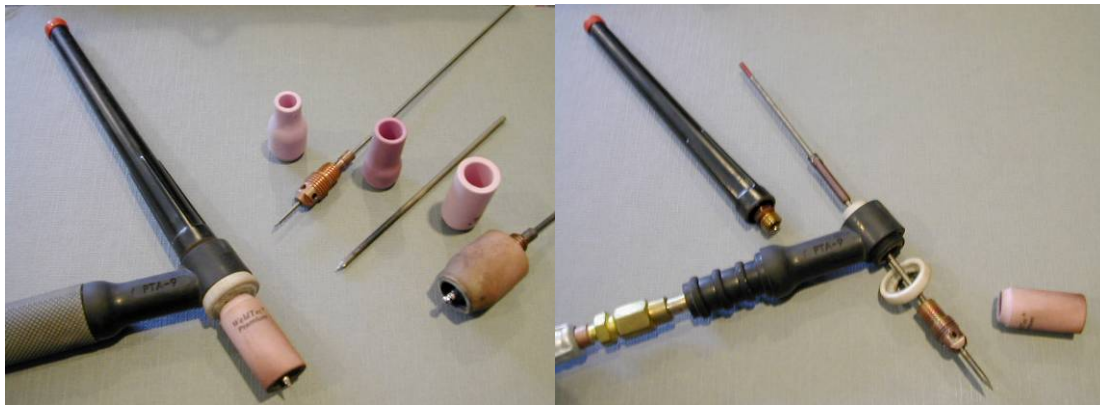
Fotografía de una pistola de soldadura TIG junto con los electrodos empleados [108][109].
